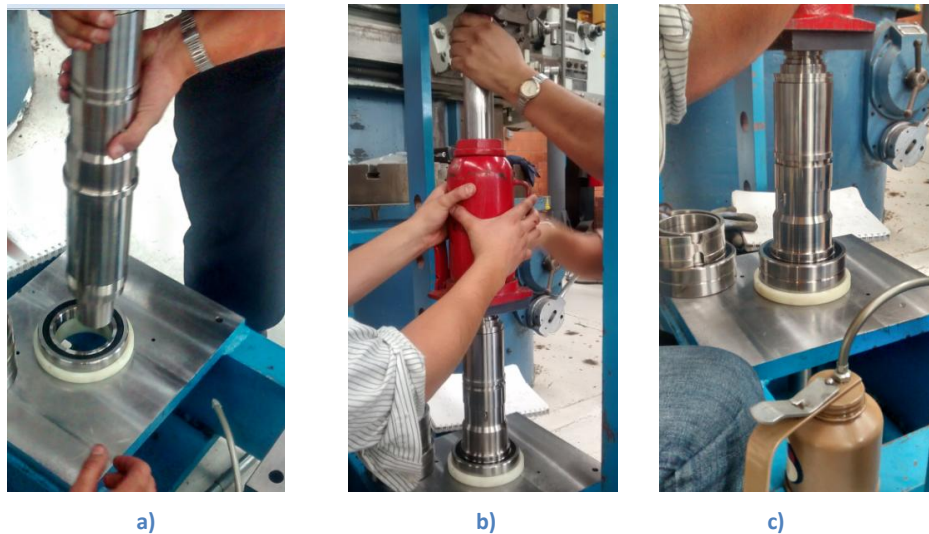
a) Primer rodamiento, b) Ingresando rodamiento con gato hidráulico, c) ingresando segundo rodamiento.
